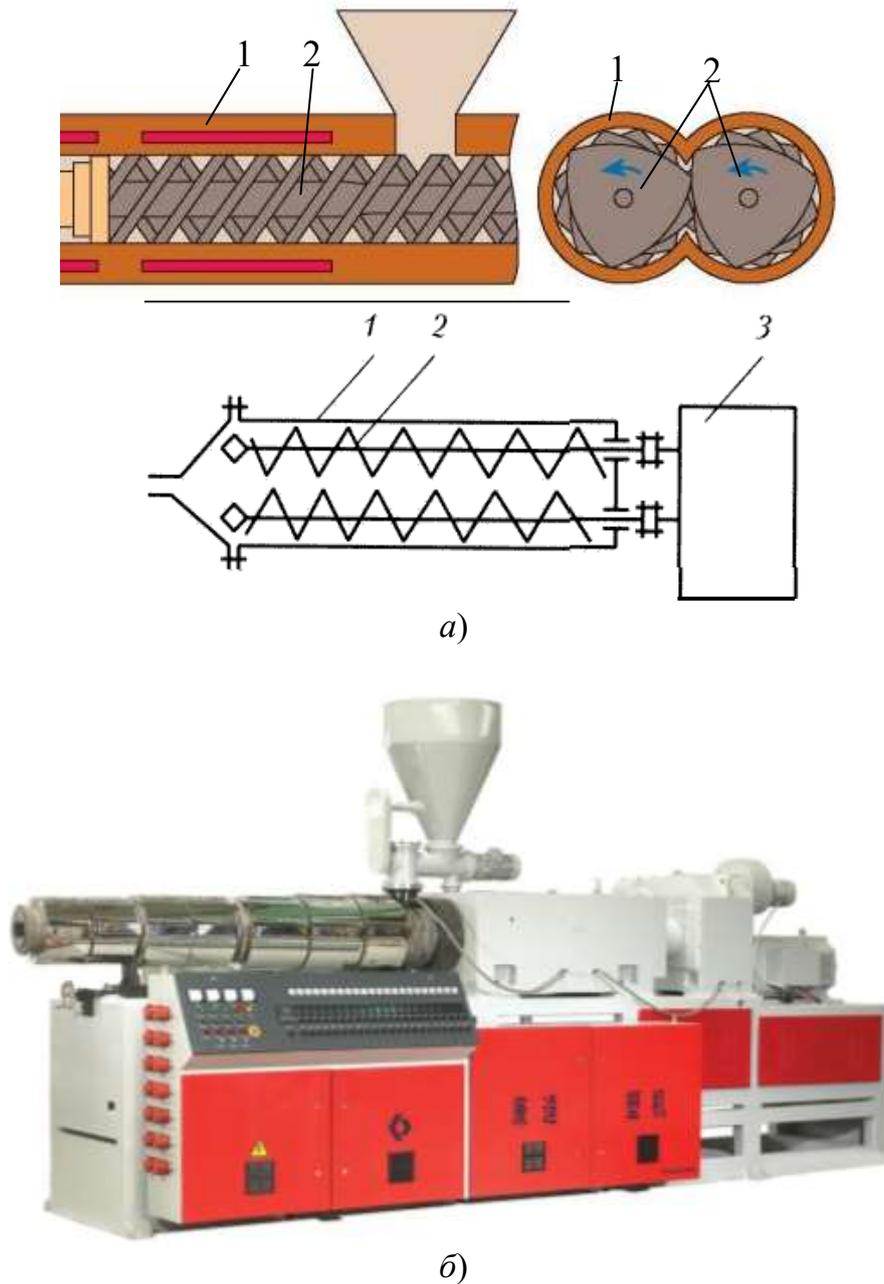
Двухшнековый экструдер: а – схема: 1 – корпус; 2 – шнек; 3 – привод;
